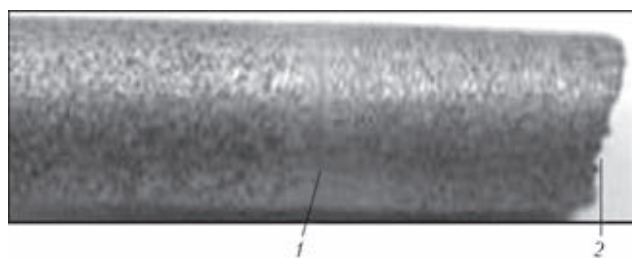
Вид образца после испытаний на растяжение: 1 — сварной шов; 2 — зона разрушения
